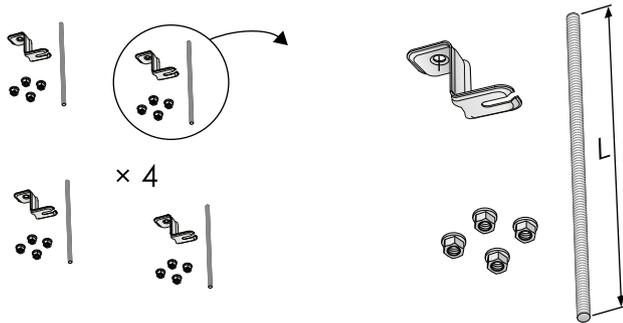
Montageteil SYST MS M8-1, Deckenbefestigung und Gewindestange
